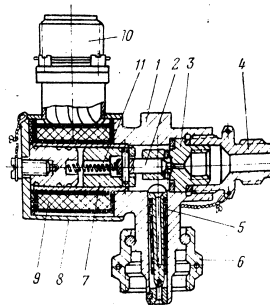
Konstrukce čerpadla PNR 10-3M.
